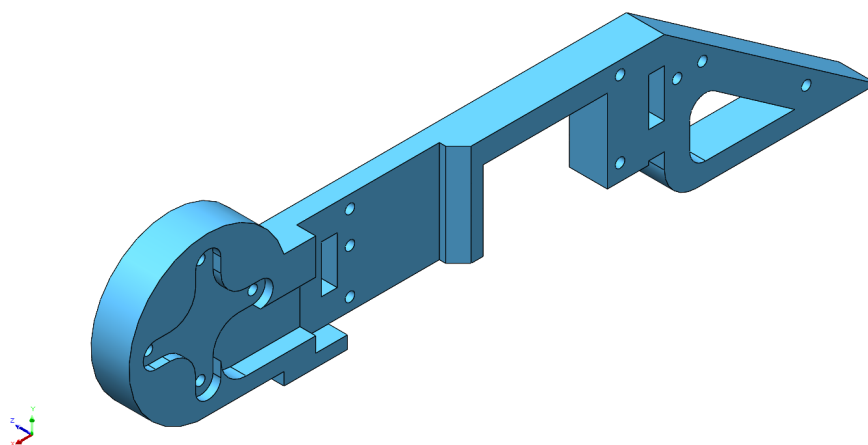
Chasis izquierdo diseñado en SolidWorks.
